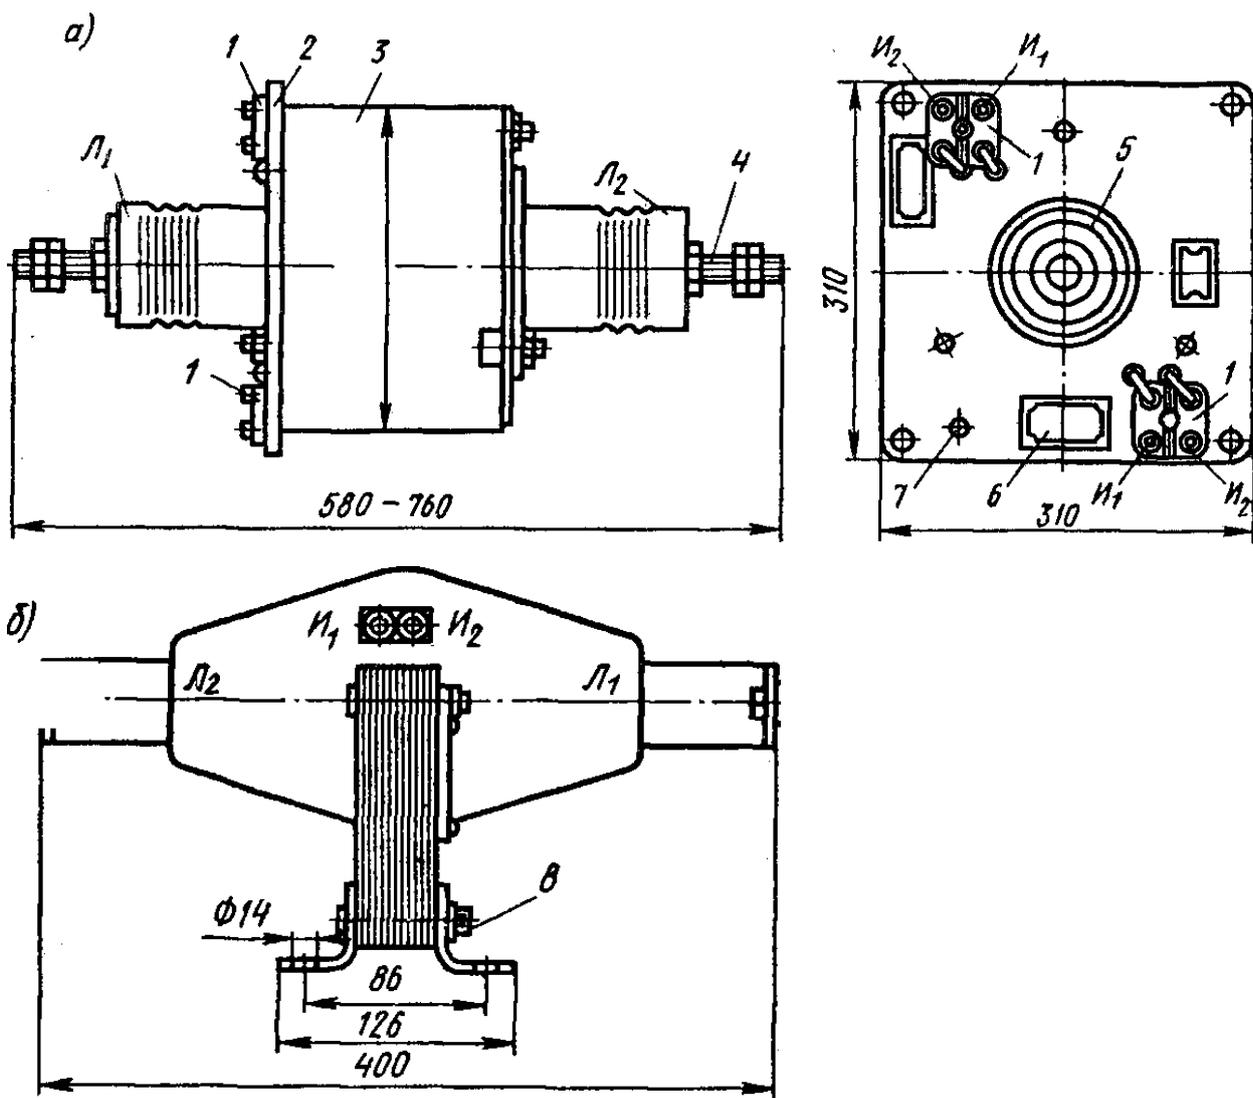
Общий вид трансформаторов тока: а - ТПОФ-10; б - ТПЛ-10; 1 - изоляционная колодка; 2 - передний фланец; 3 - кожух; 4 - стержень; 5 - изолятор; 6 - табличка с техническими данными; 7, 8 - болты заземления; Л₁, Л₂ - первичные обмотки; И₁, И₂ - вторичные обмотки
